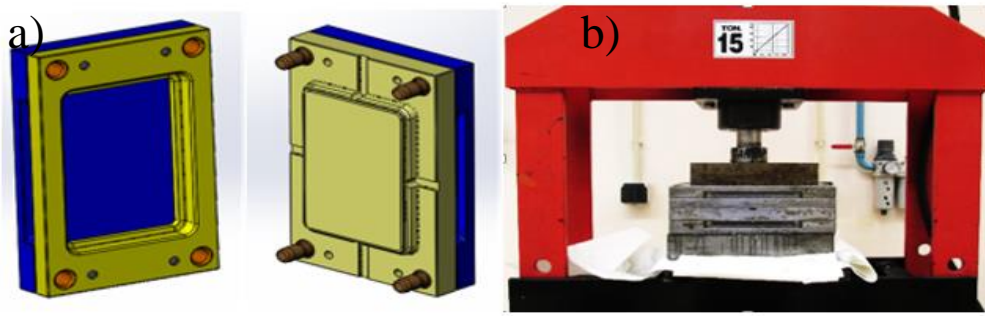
Molde de compressão metálico (Esq.); Prensa hidráulica para compressão do molde (Drt.)
